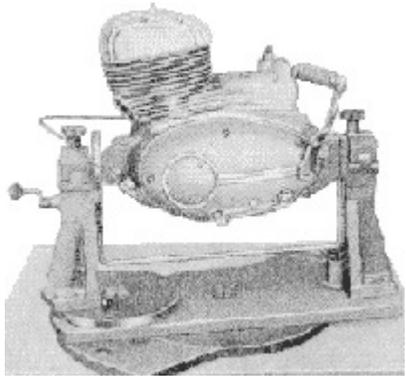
Einspannvorrichtung 05 H 8-587 mit eingespanntem ES-Motor
